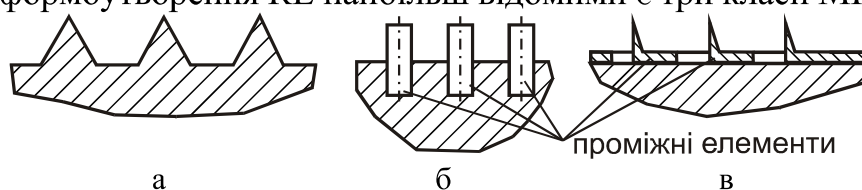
Повздовжній переріз металевих закінцівок з різними варіантами утворення трансверсальних КЕ: а – монолітні; б – циліндричні; в – листові типу “канцелярська кнопка”
